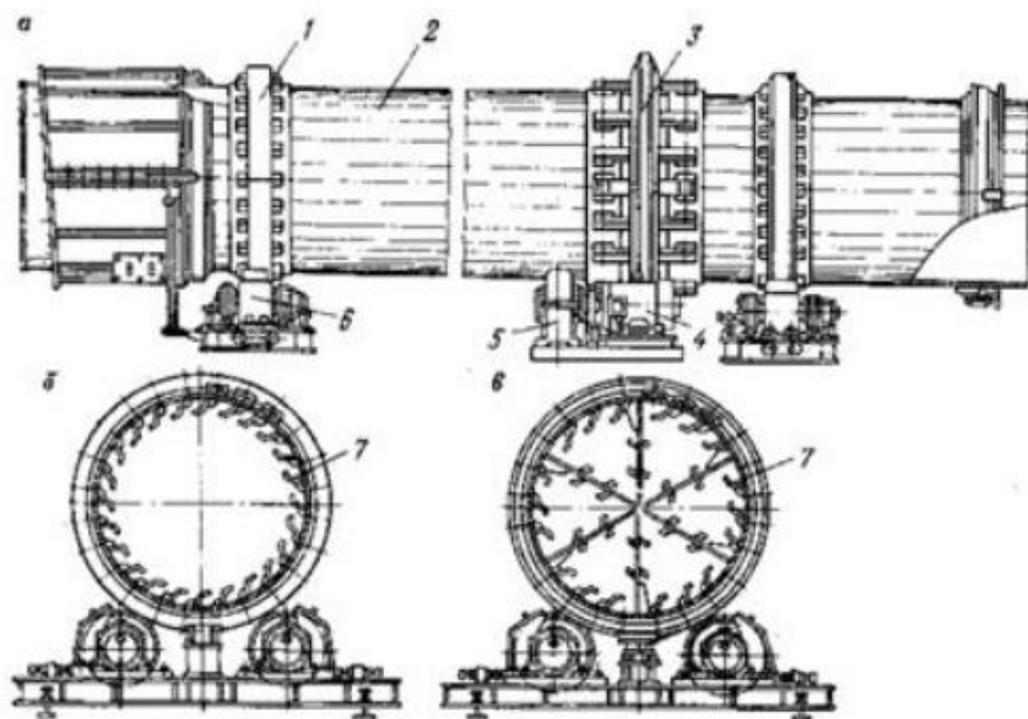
Сушильный барабан [6]: а – общий вид; б – лопастная насадка; в – секторная насадка; 1 – бандажи; 2 – барабан; 3 – зубчатый венец; 4 – редуктор; 5 – электродвигатель; 6 – опорные ролики; 7 – насадки
